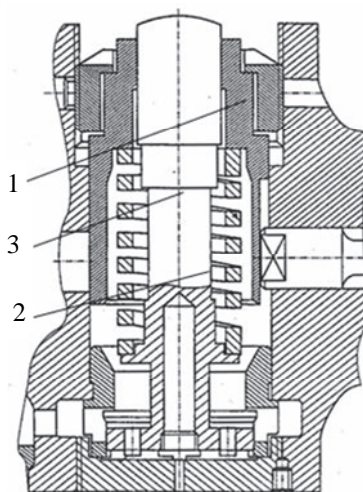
Центробежный выключатель с точеной пружиной: 1 – гайка; 2 – пружина; 3 – боек
